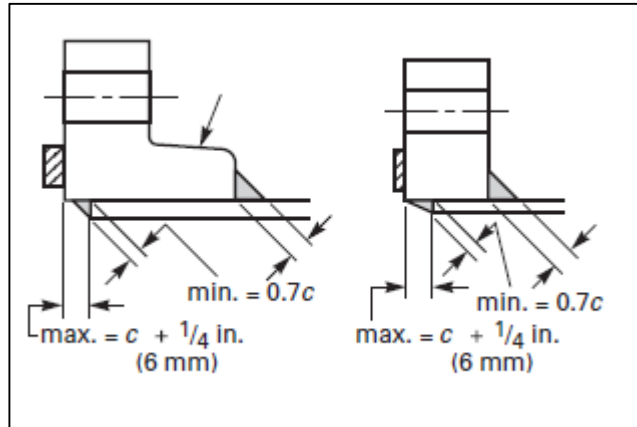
Dimensiones requeridas de soldadura en junta
